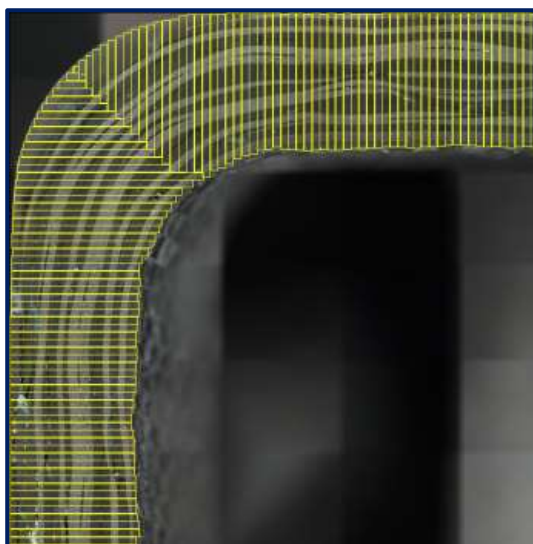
Subdivisión de la sección transversal en U en áreas rectangulares de 0,2 mm de ancho.
